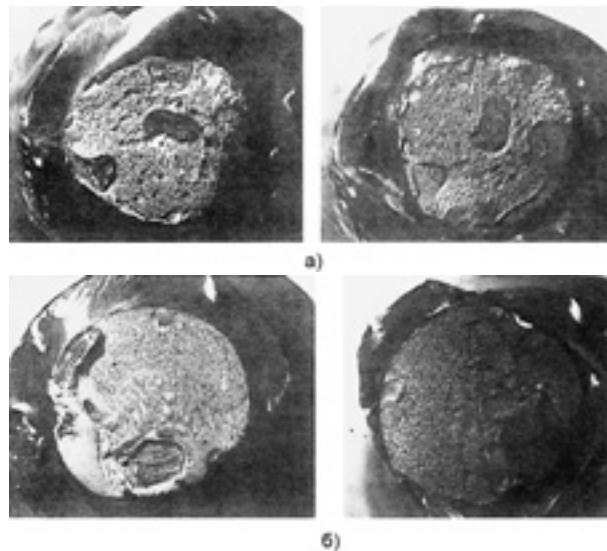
Разрушенные образцы после пайки (справа — твердый сплав, слева — стальная державка): а — пластина; б — полукольцо
